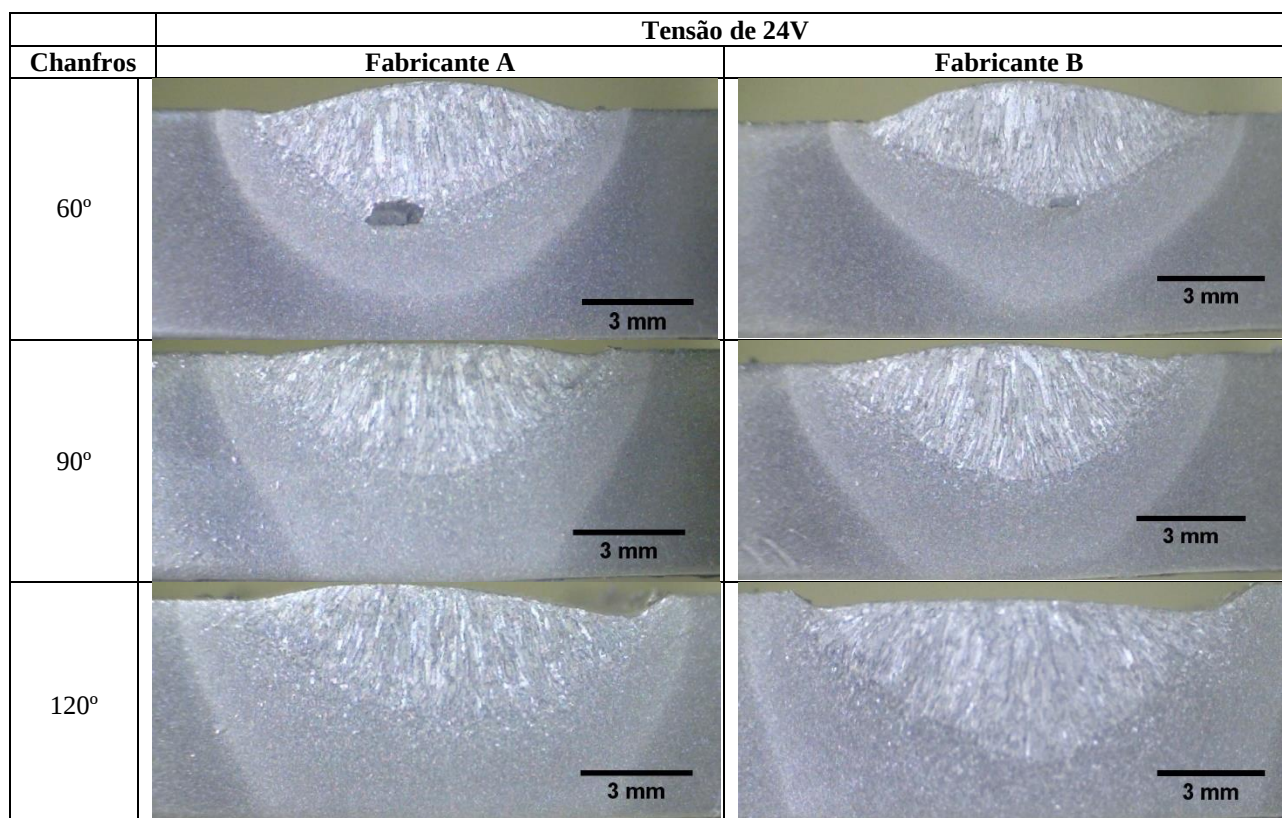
Seção transversal dos cordões de solda com tensão de 24V dos fabricantes A e B.
